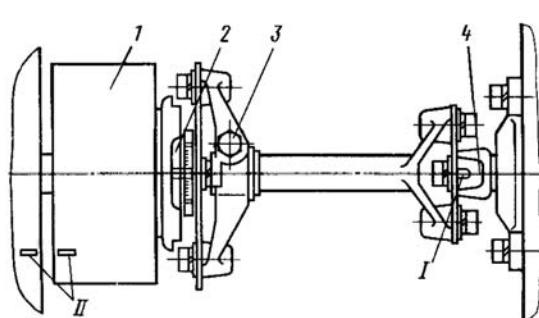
Установка начала впрыска топлива в первом цилиндре двигателя по меткам:
